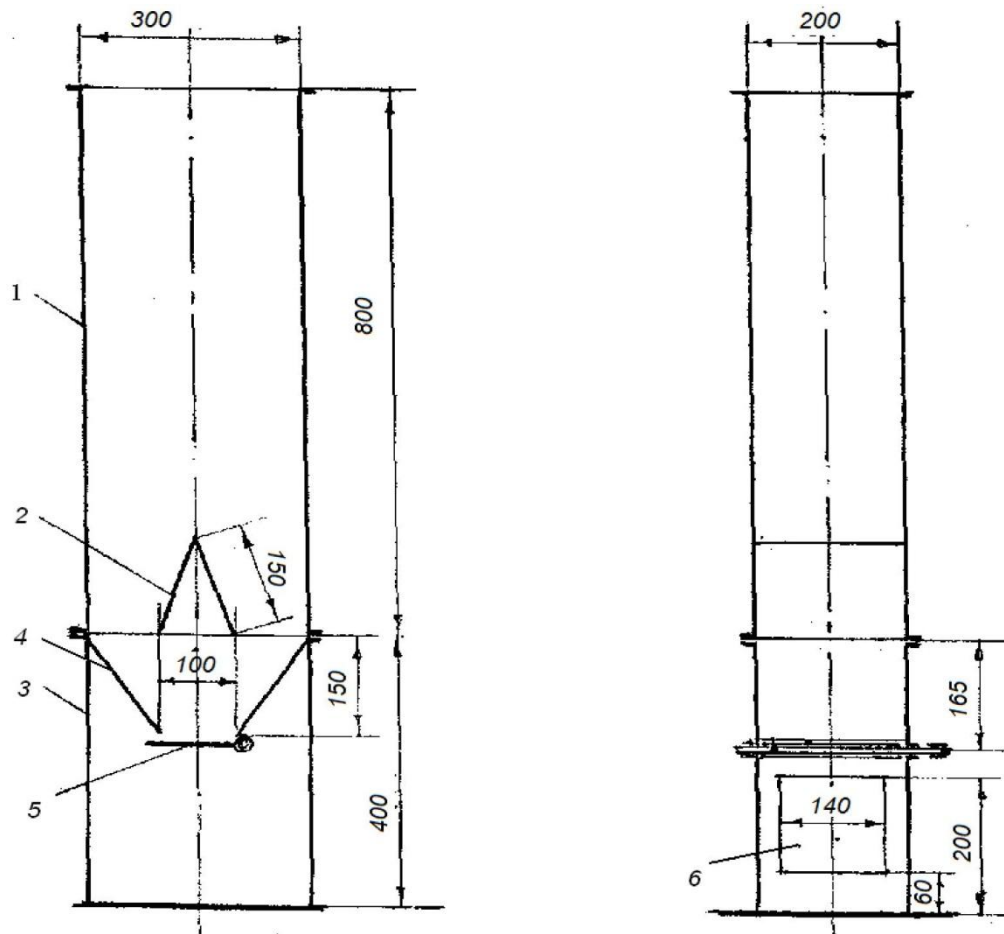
Лабораторная модель камеры с распределительным устройством 1 - верхняя камера; 2 - делитель кокса; 3 - нижняя камера; 4 - направляющие кокса; 5 - шибер поворотный; 6 - окно для выгрузки кокса
